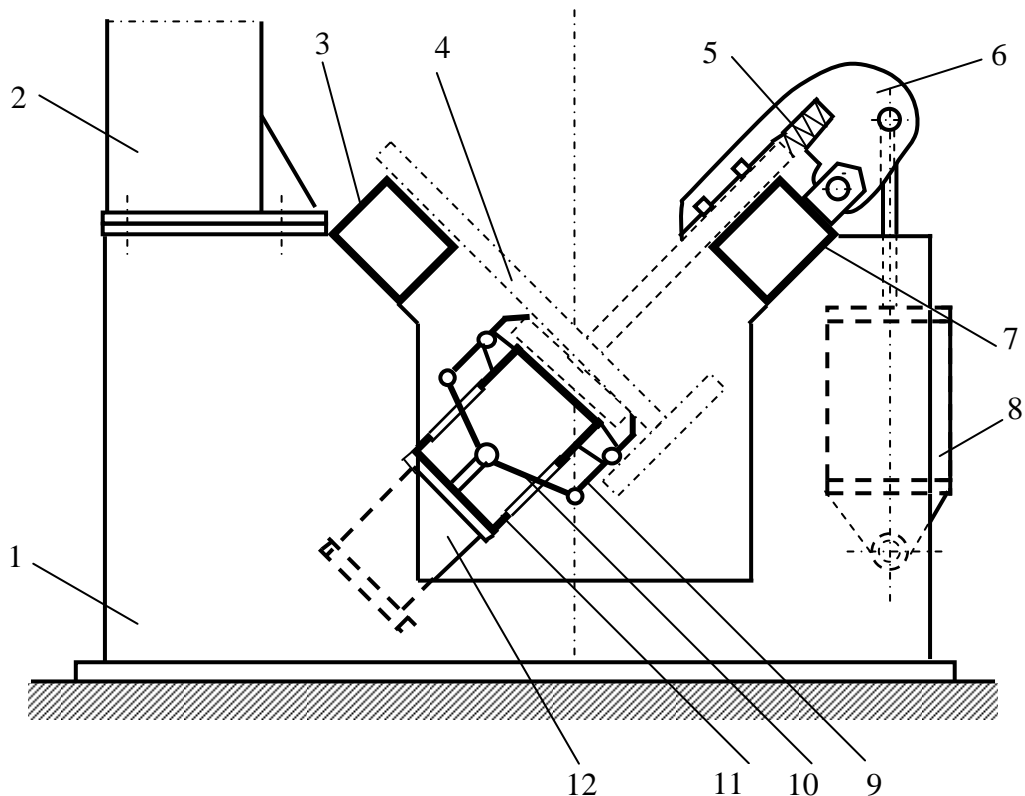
Схема кондуктора-кантувача для складання і зварювання таврових балок: 1-станина; 2- колона для зварювального автомата; 3- ліва опорна балка; 4 – балка, що зварюється; 5- пружина; 6- верхній притискач; 7- права опорна балка; 8 – хитний гідроциліндр; 9- кліщовий захват; 10 - система ламких важелів; 11 - поворотна опорна балка; 12- пневмоциліндр.
